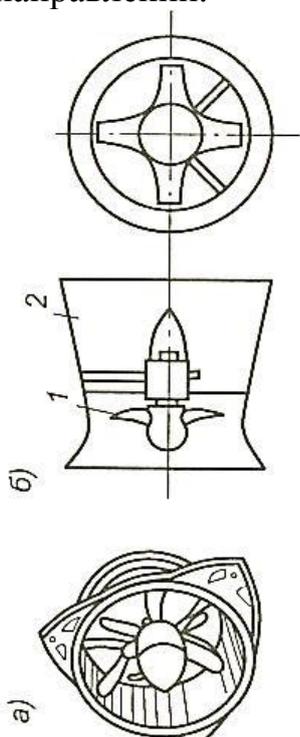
а) Общий вид; б) схема устройства осевого вентилятора
